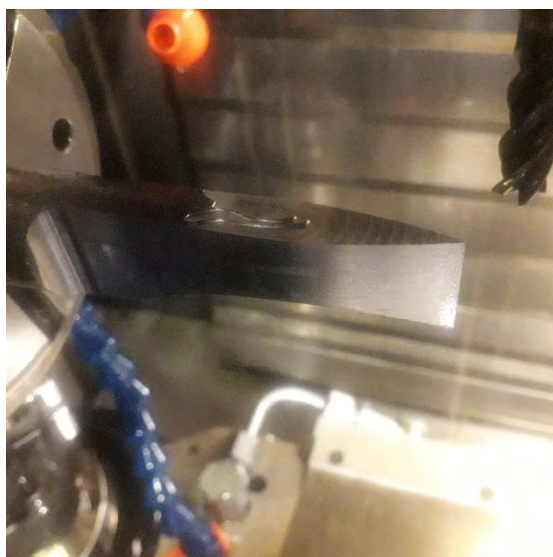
Черновое фрезерование выпуклой части наружной поверхности с поворотом заготовки на 180° на $\frac{1}{2}$ ее длины
